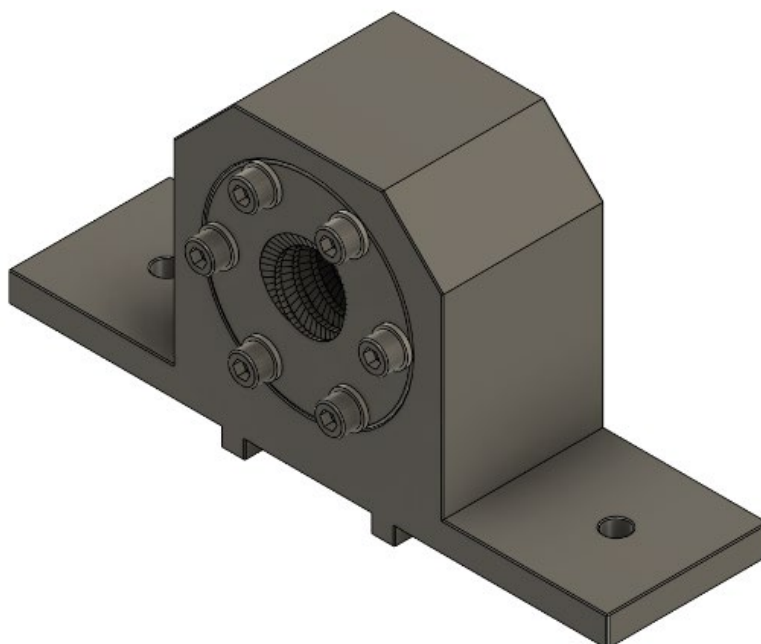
/ Linearantrieb Laufmutter mit Lager
